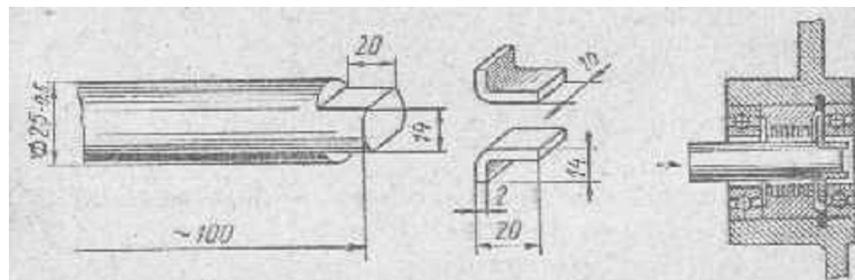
Приспособление для снятия подшипника коленчатого вала
